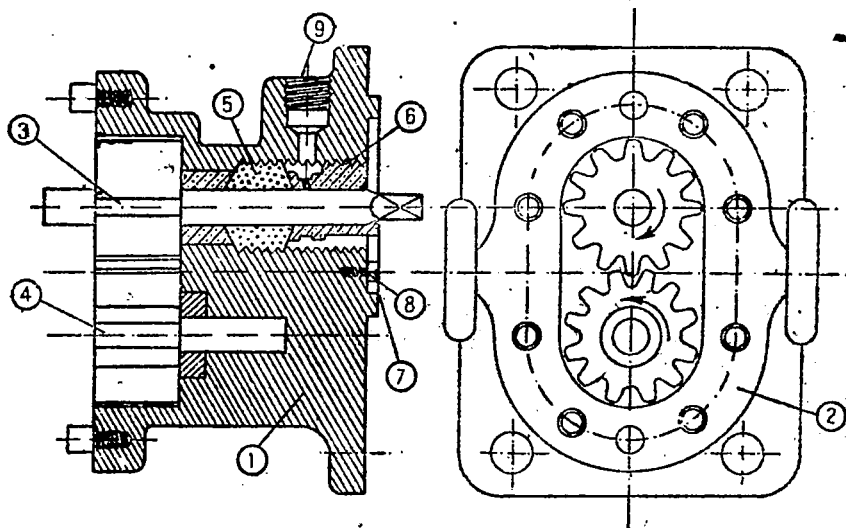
Шестеренчатая бензиновая помпа мотора М-5. 1. Корпус помпы. 2. Крышка. 3. Шестерня ведущая. 4. Шестерня ведомая. 5. Уплотняющая набивка. 6. Проока-подшипник (букса). 7. Фланец пробки. 8. Стопорный вилт. 9. Пробка для пополнения и подачи масла.
